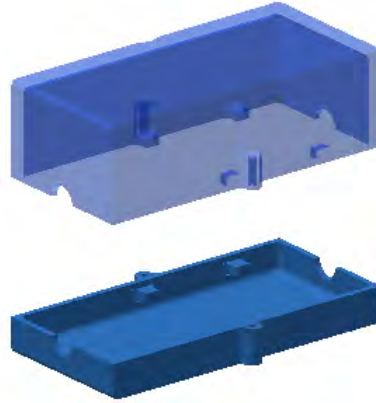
Modelo 3D de la pieza final con su estructura abierta
